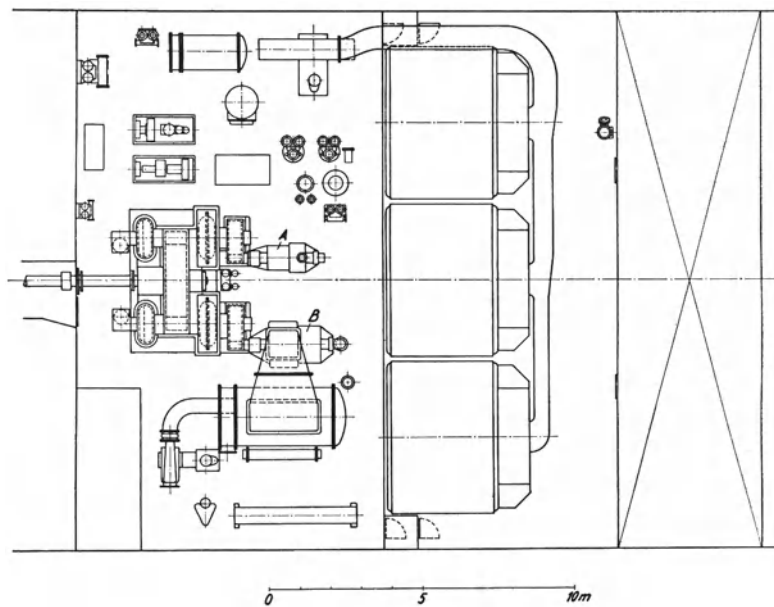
Turbinenanlage mit hydromechanischem Getriebe für einen Frachtdampfer von 9500 t Tragf.
